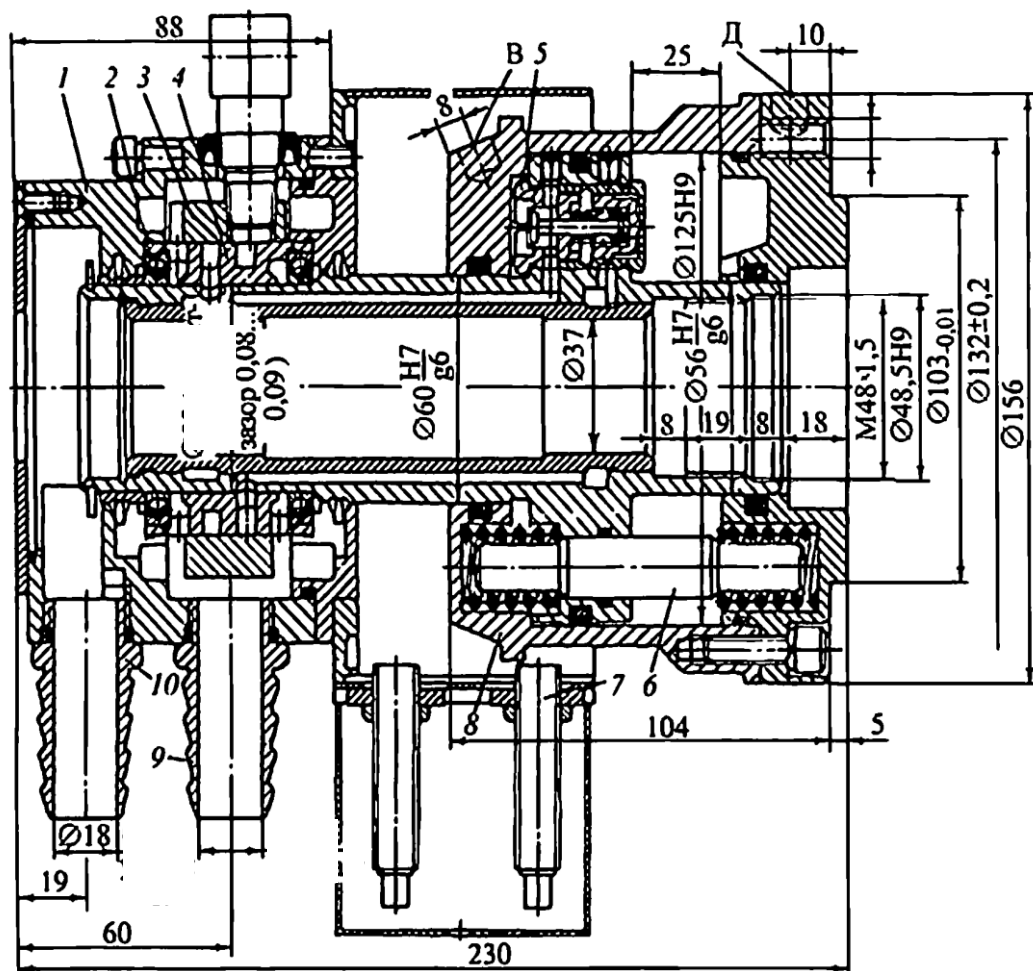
Типова конструкція порожнистого обертового гідроциліндра з маслопідвідним пристроєм
